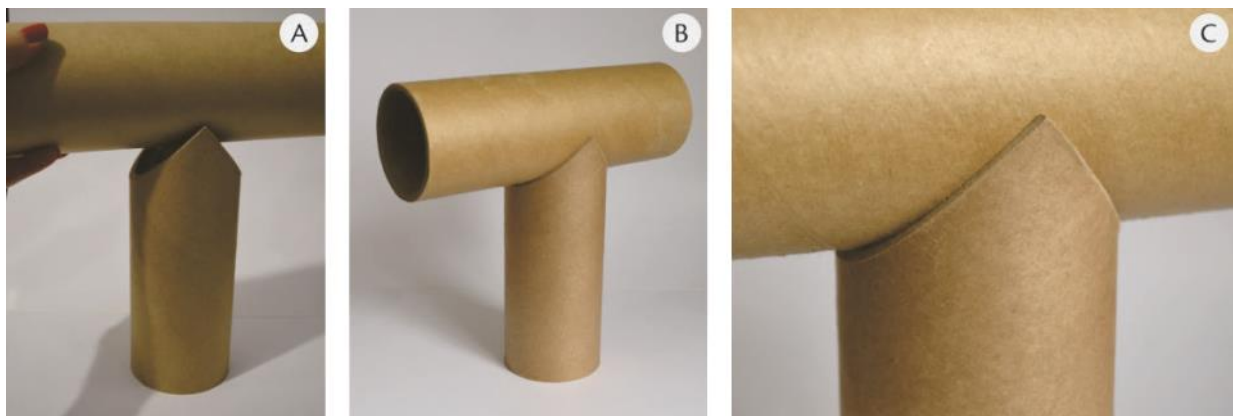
União perpendicular boca de peixe. (A) Colagem sendo realizada; (B) União finalizada; (C) Detalhe.
